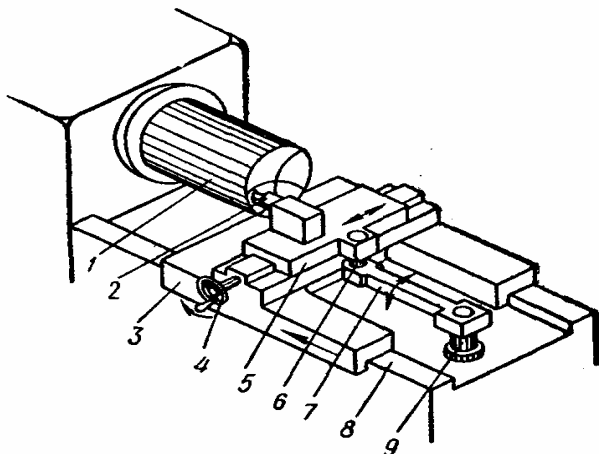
Схема обработки вогнутой сферической поверхности на токарном станке с построителем
